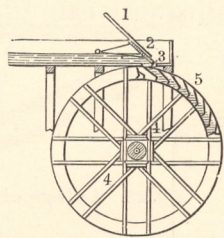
Oberschlächtiges Wasserrad mit Spansschütze.
